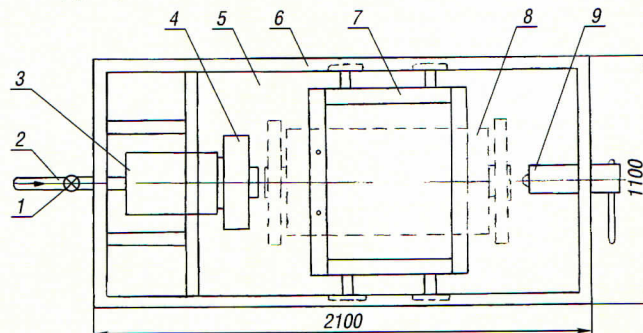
Установка разборки-сборки мотор-компрессора и мотор-вентилятора электровоза ВЛ80С:
